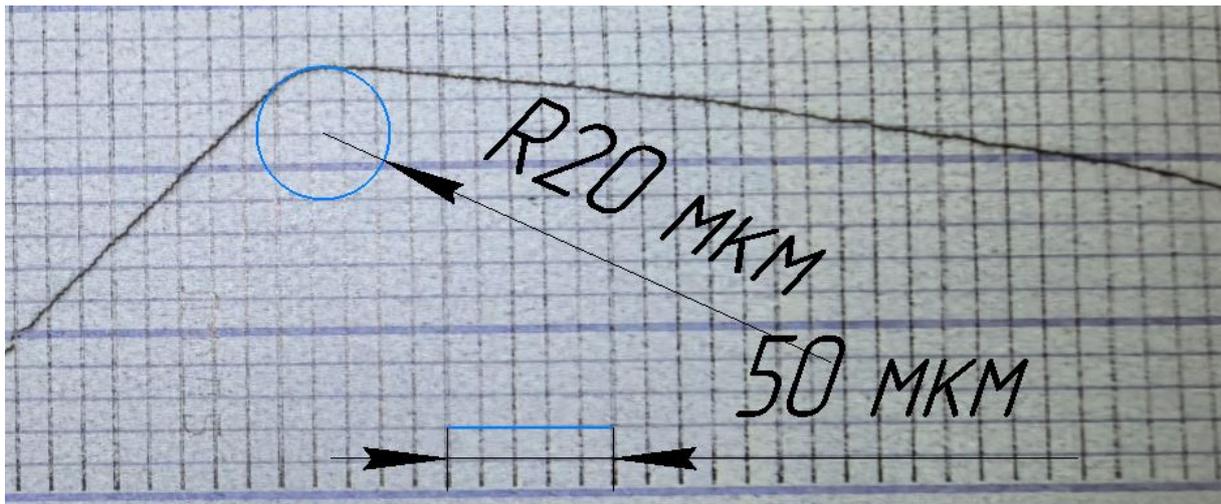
Пример измерения радиуса округления режущей кромки боковой стороны резьбовой фрезы.
